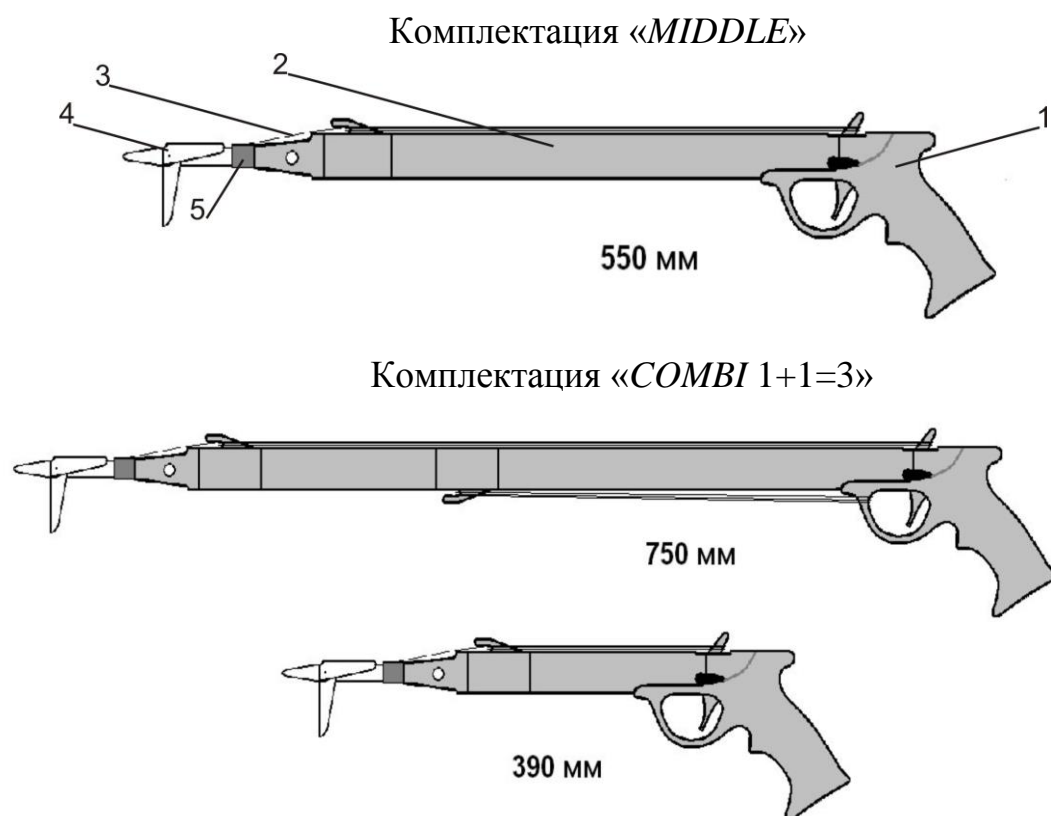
1-рукоятка, 2-ресивер, 3-линь, 4-гарпун, 5-втулка скользящая
